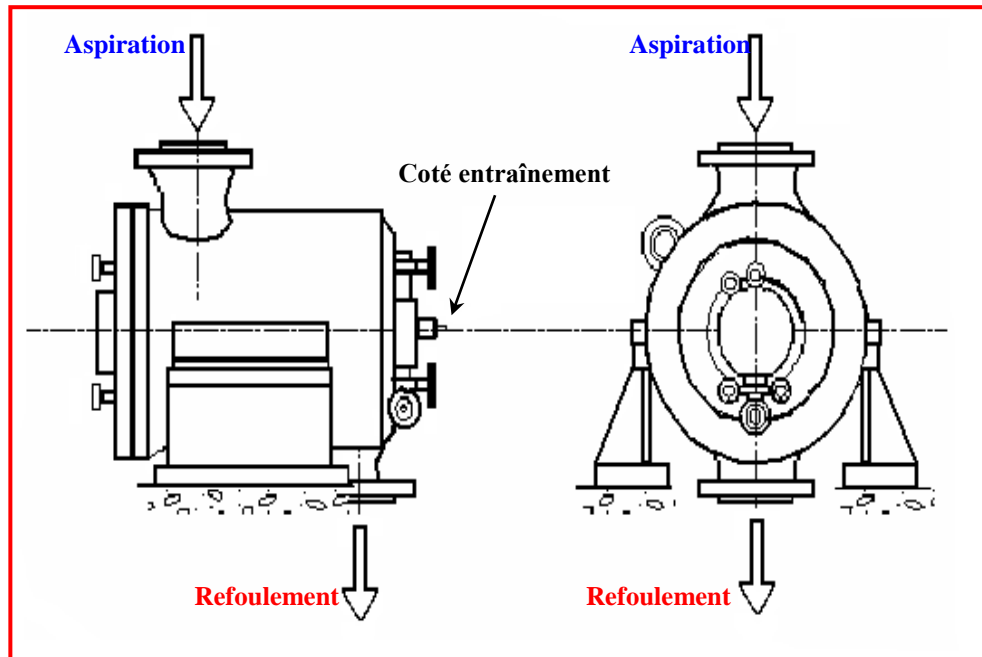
Compresseur à plan de joint vertical (Type Barrel).
